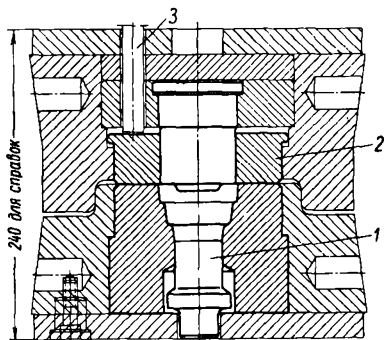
Вставка для закрытой штамповки в блоке с двойным противодействующим устройством
